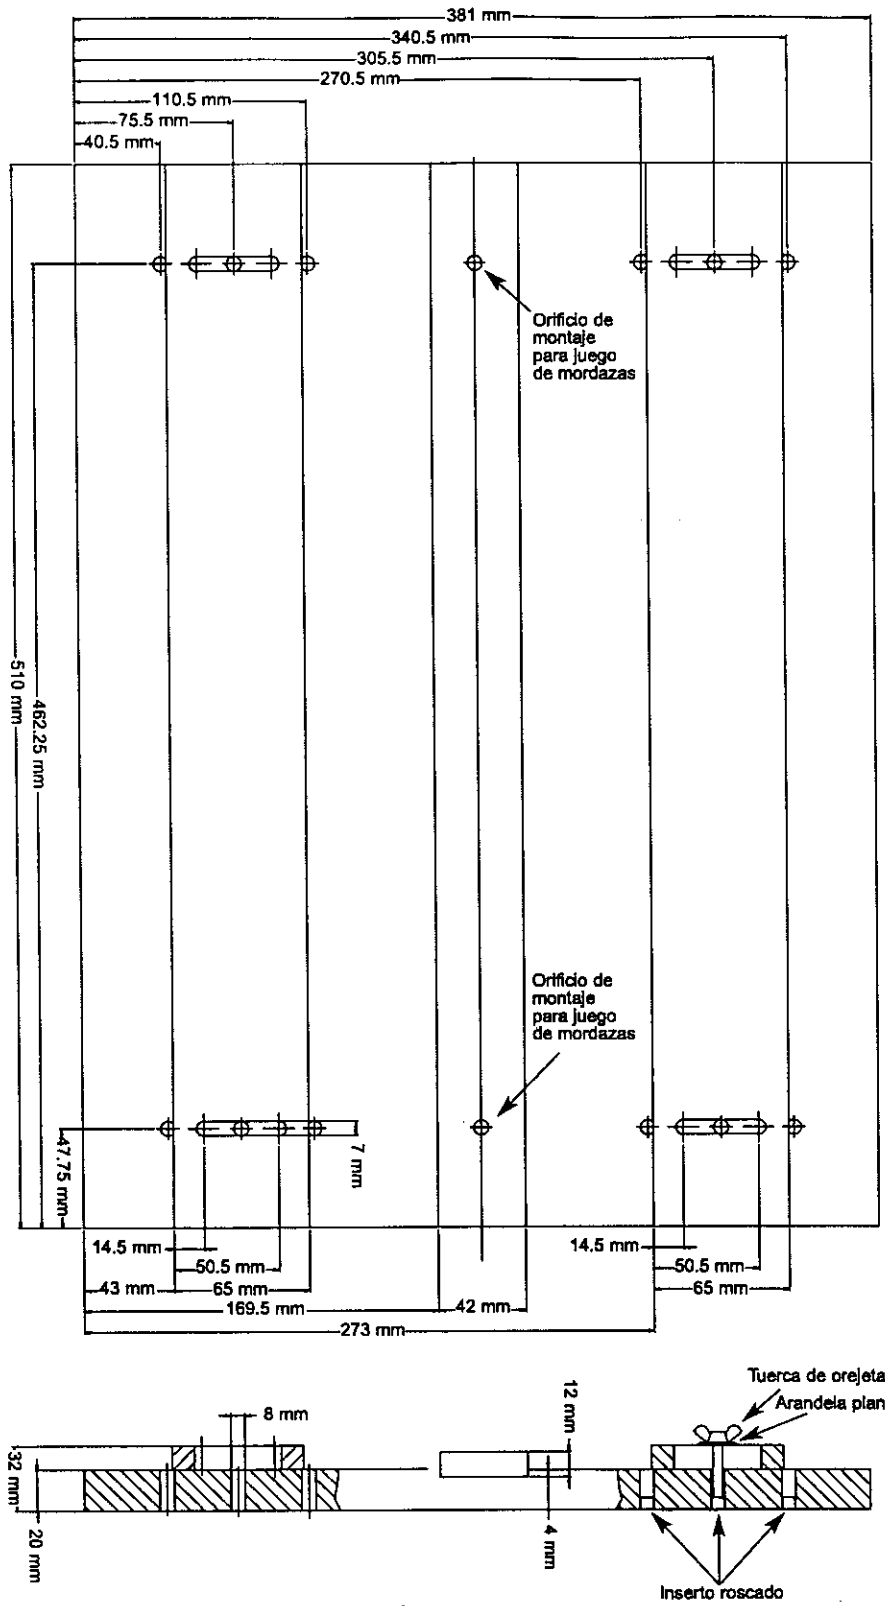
Dimensiones para la Mesa Auxiliar y Rebordes Guía
